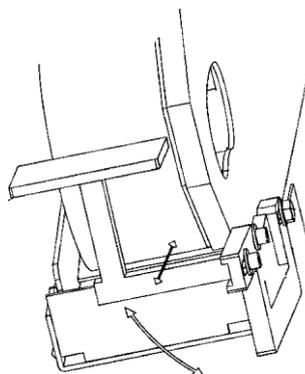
Регулировка рабочих поверхностей с задней стороны
